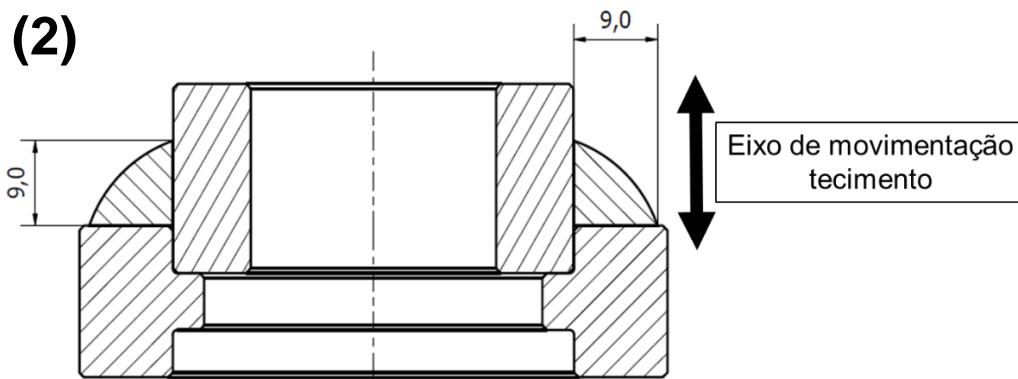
(2) - Passe único com tecimento (dimensões em mm)
